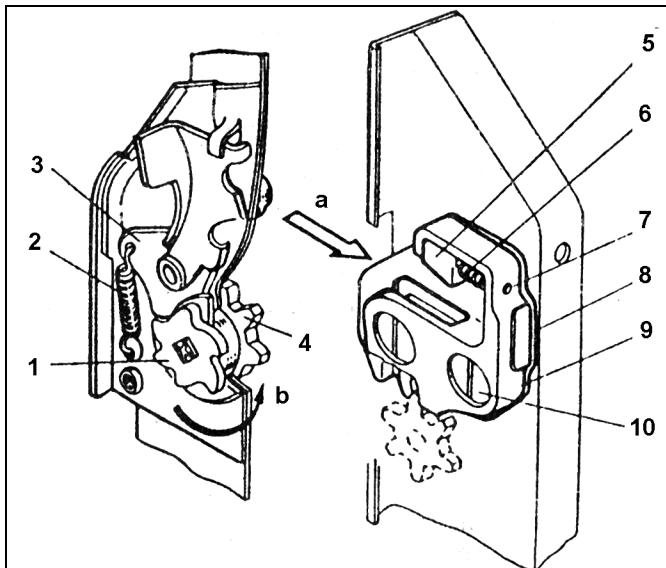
Положение замка и защелки при закрытии двери: 1 — храповик; 2 — пружина; 3 — собачка храповика; 4 — ротор замка; 5 — сухарь; 6 — пружина сухаря; 7 — ось; 8 — прокладка защелки; 9 — защелка; 10 — винт.
